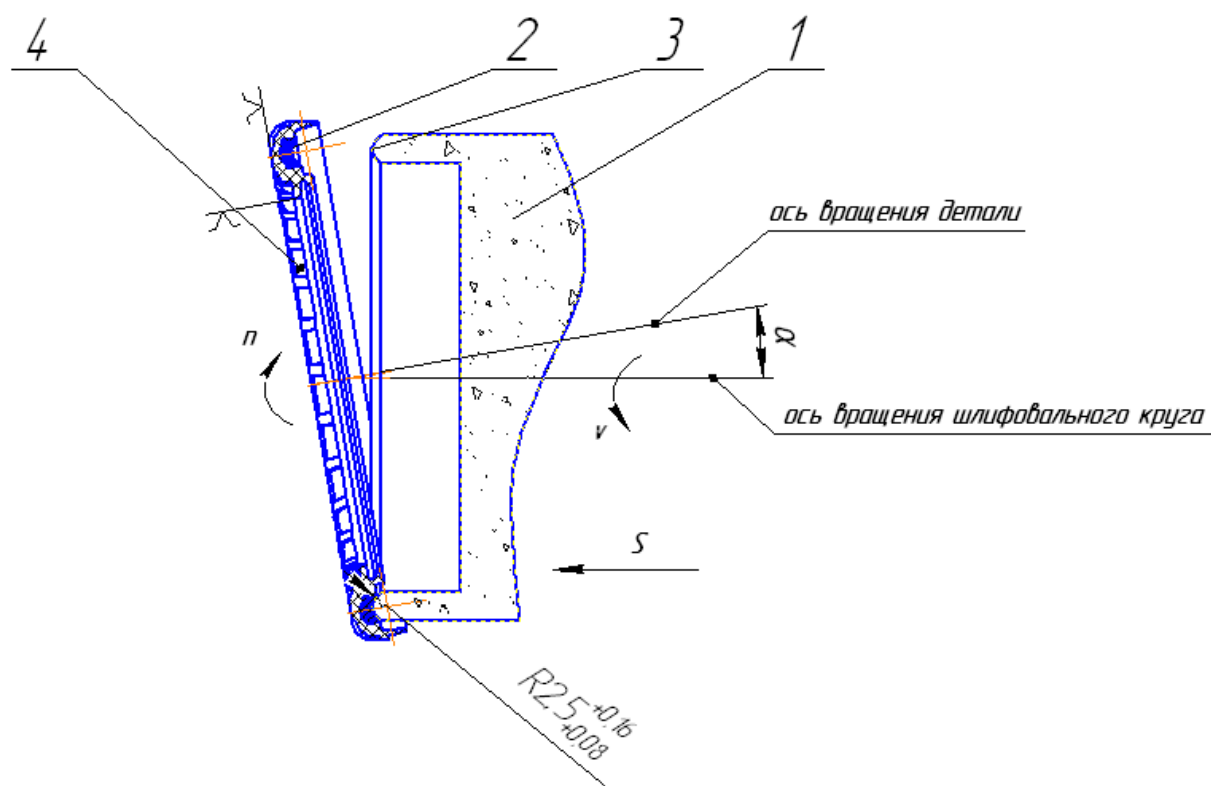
Схема процесса шлифования дорожек качения упорных подшипников
